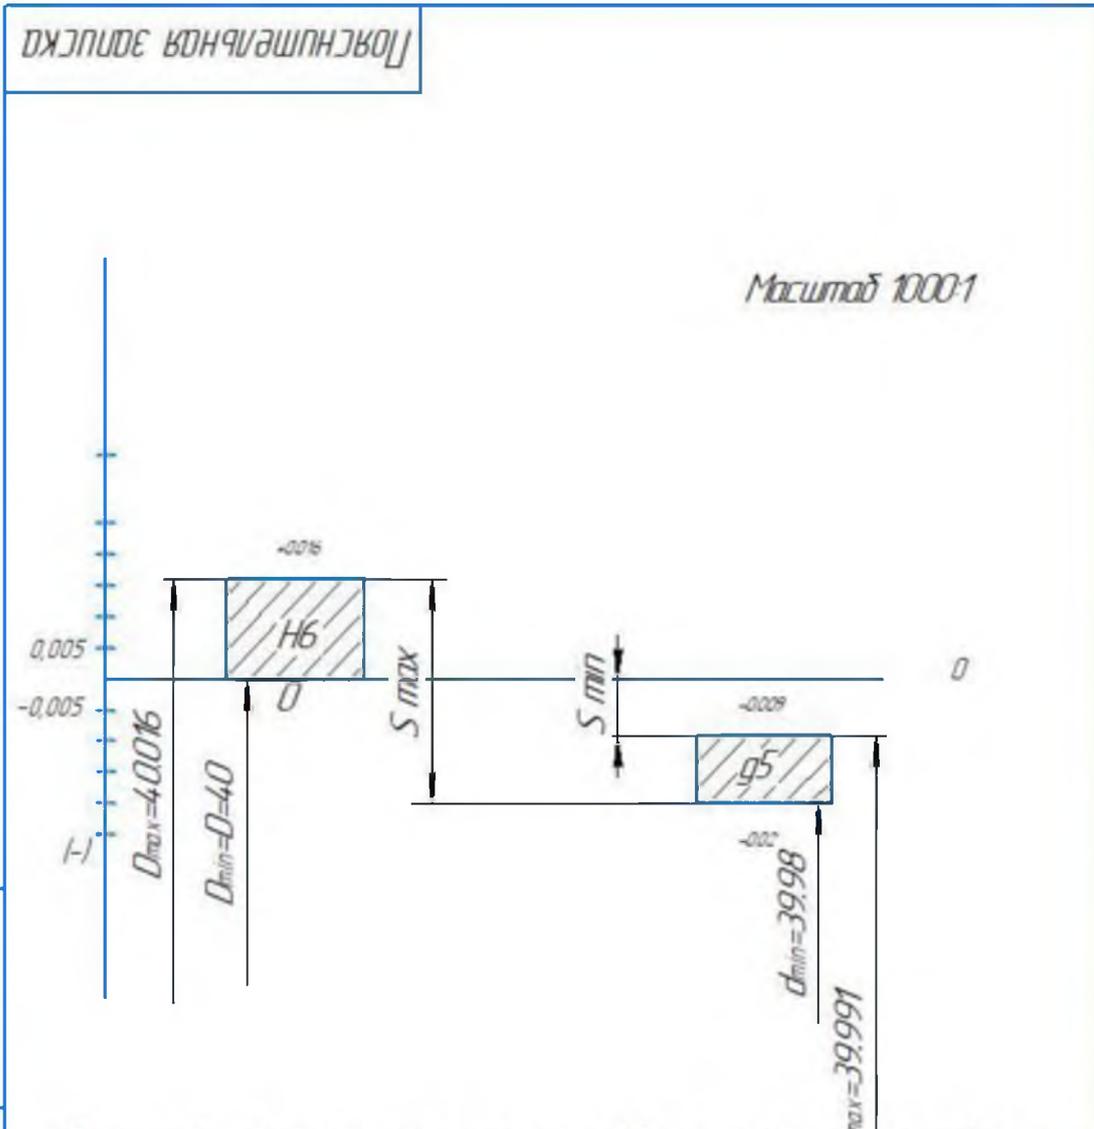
Схема расположения полей допусков в системе отверстия.
